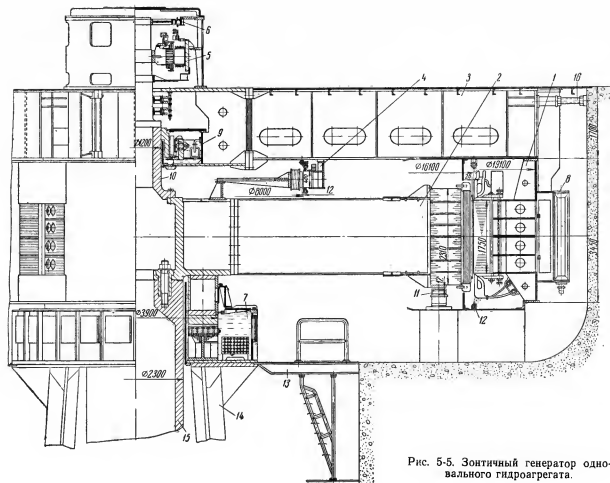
Зонтичный генератор однофазного гидроагрегата.
